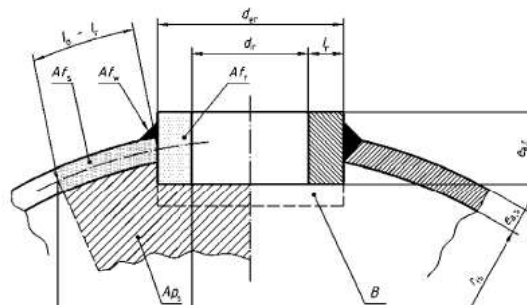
Soldadura de conexiones hidráulicas
